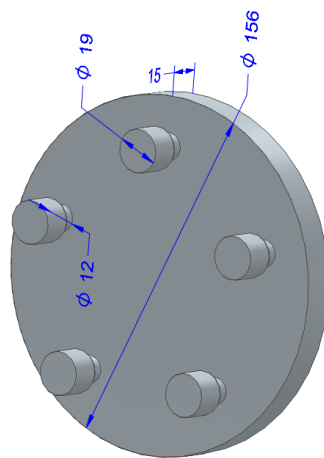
Model 3D de la boixa amb el conjunt de cargols i casquets
